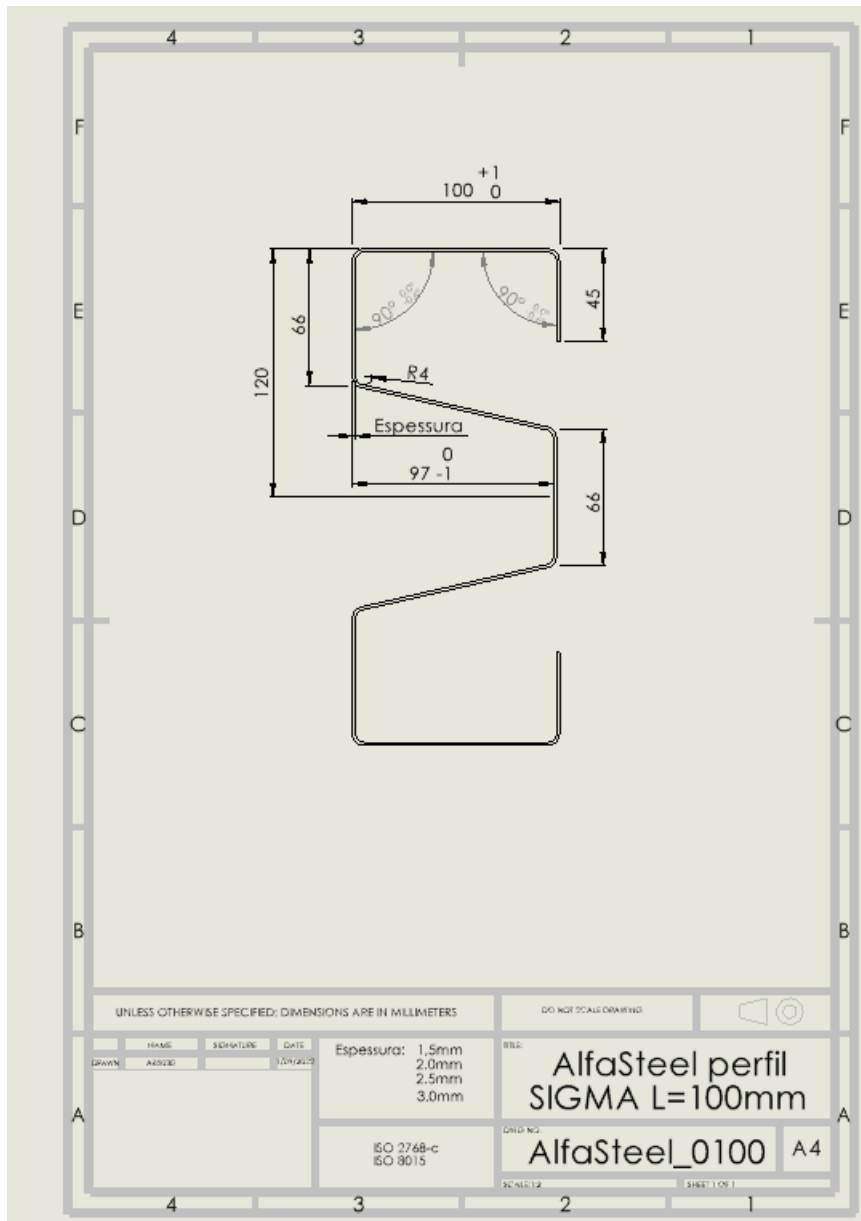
Desenho técnico perfil de Largura = 100 mm
